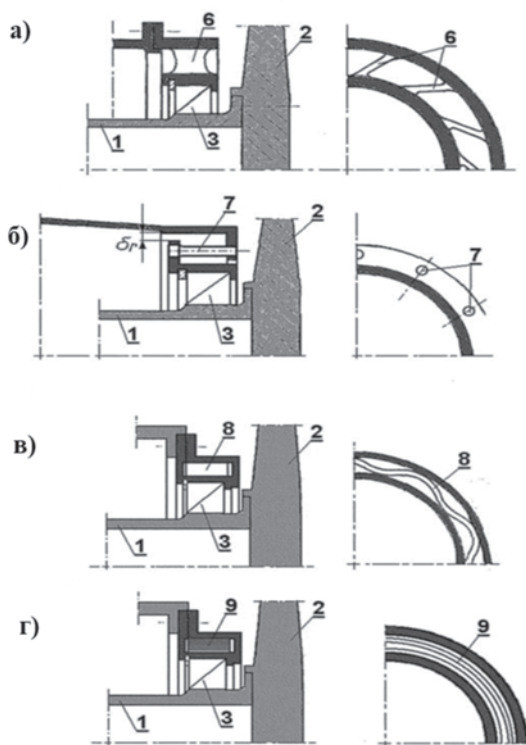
Принципы построения гибких опор роторов: а) с гибким ребром; б) с восприимчивыми кольшками; в) с волнистой гибкой вставкой; г) с пакетом жестяных вставок 1 - вал; 2 - опорный диск ротора; 3 - подшипник; 6 - гибкое ребро; 7 - гибкие заглушки; 8 - волнистая гибкая вставка; 9 - пакет с оловянной вставкой
